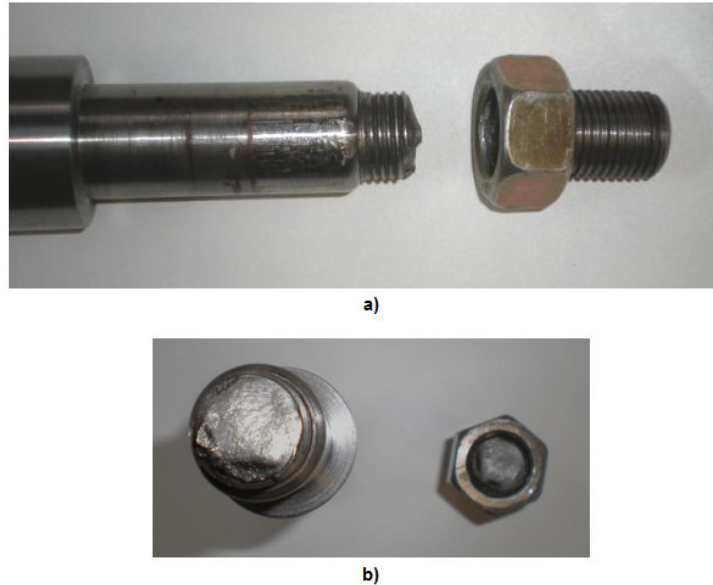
Zona de rotura da amostra após ensaio de fadiga, a) vista longitudinal, b) secção transversal.
